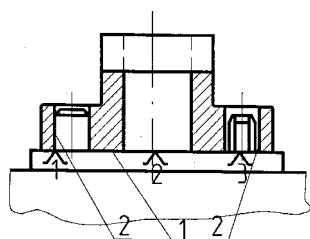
Базирование корпусной заготовки на плоскость и два отверстия
